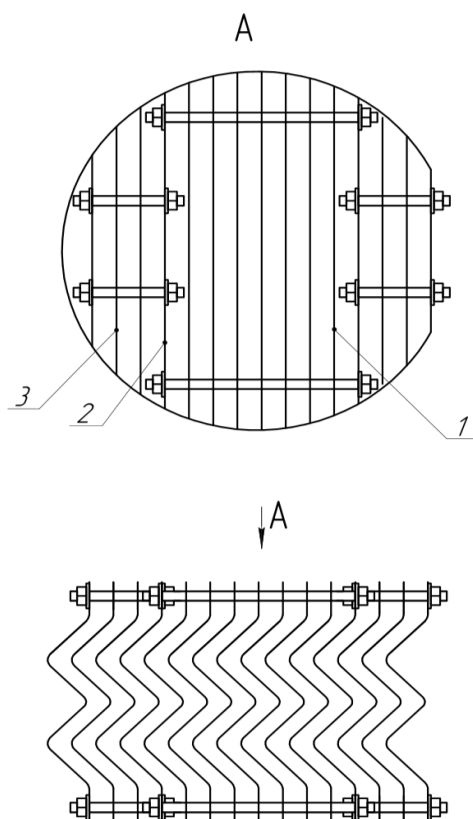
Общий вид и компоновка пакета жалюзи:
